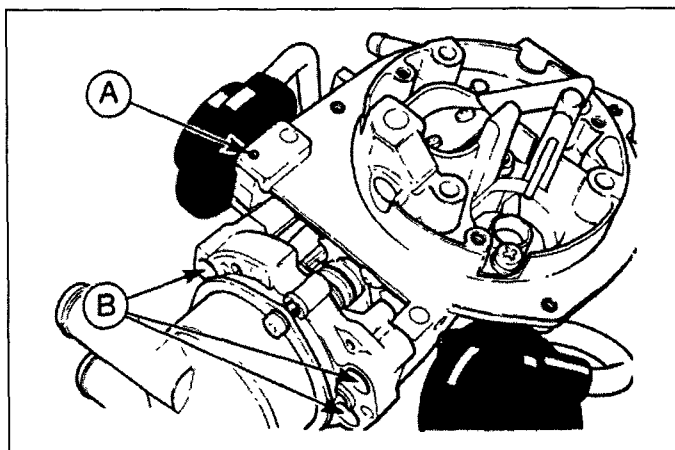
а. Диафрагменный привод пускового устройства и корпус рычага
